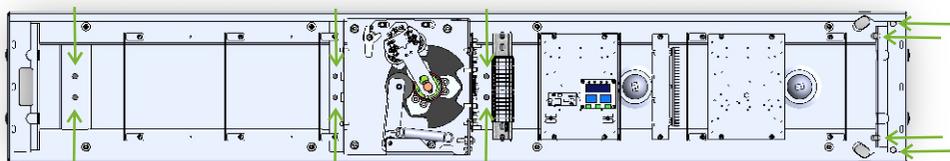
Отверстия для крепления корпуса механизма
